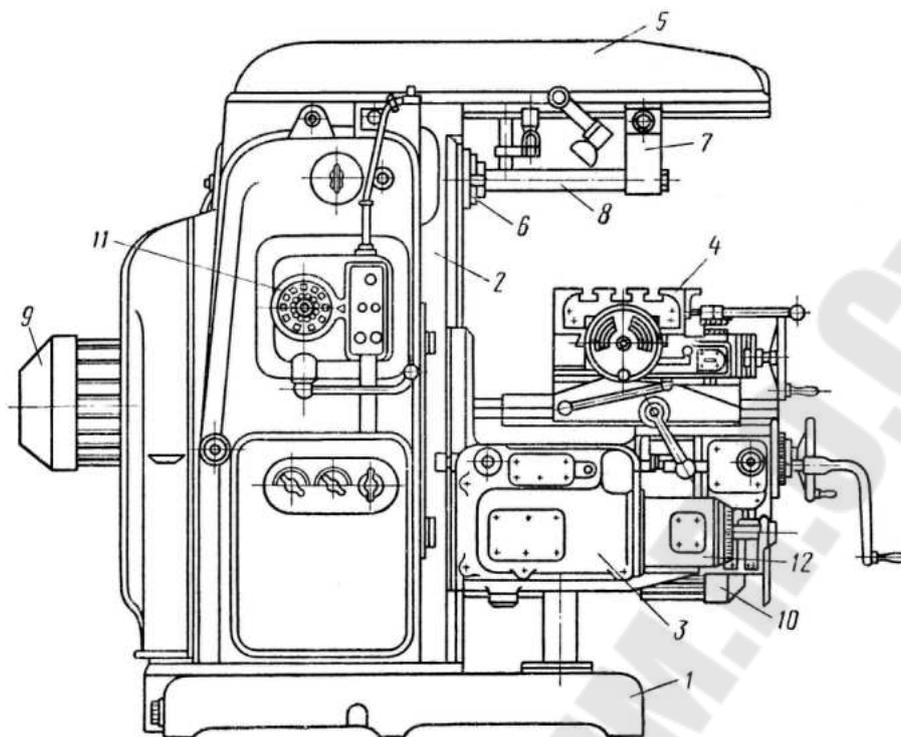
Профильная проекция общего вида горизонтально-фрезерного станка 6P82:
